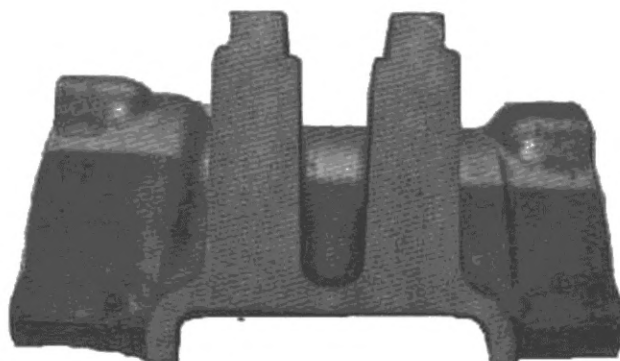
Схема вырезки проушины корпуса редуктора
